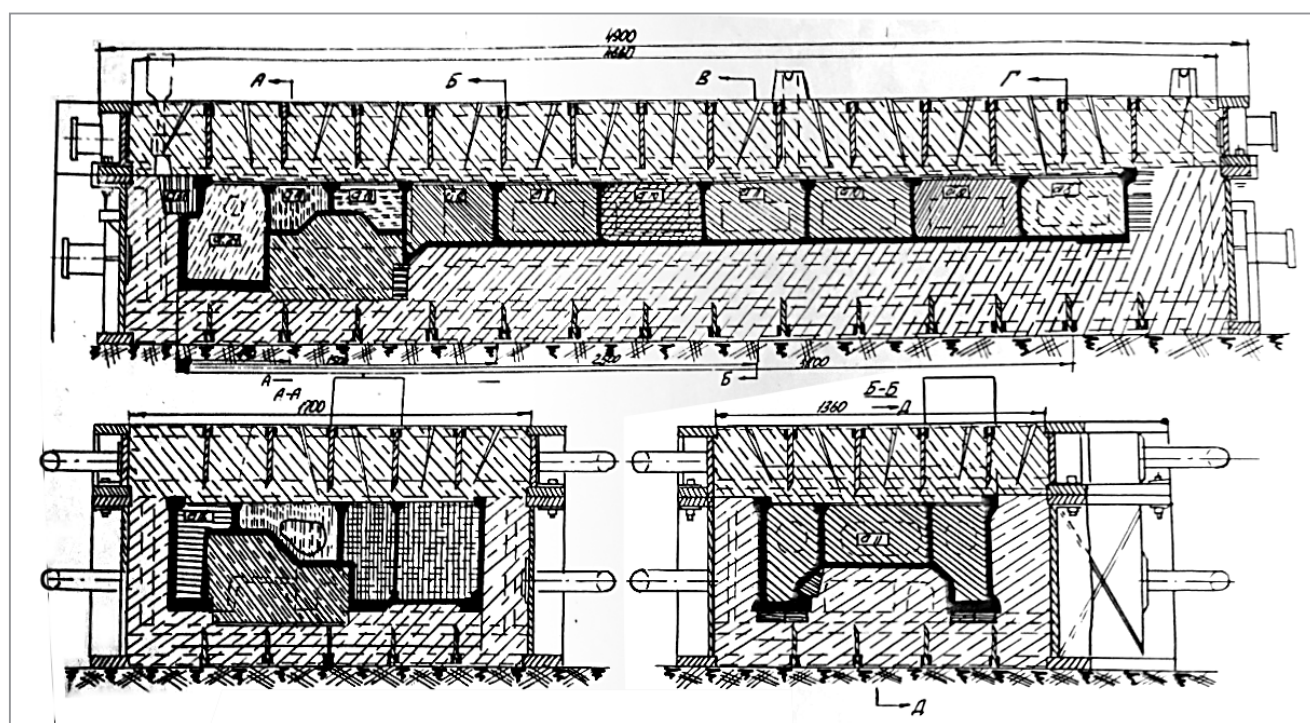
Схема сборки формы станины расточного станка с верхней опокой
